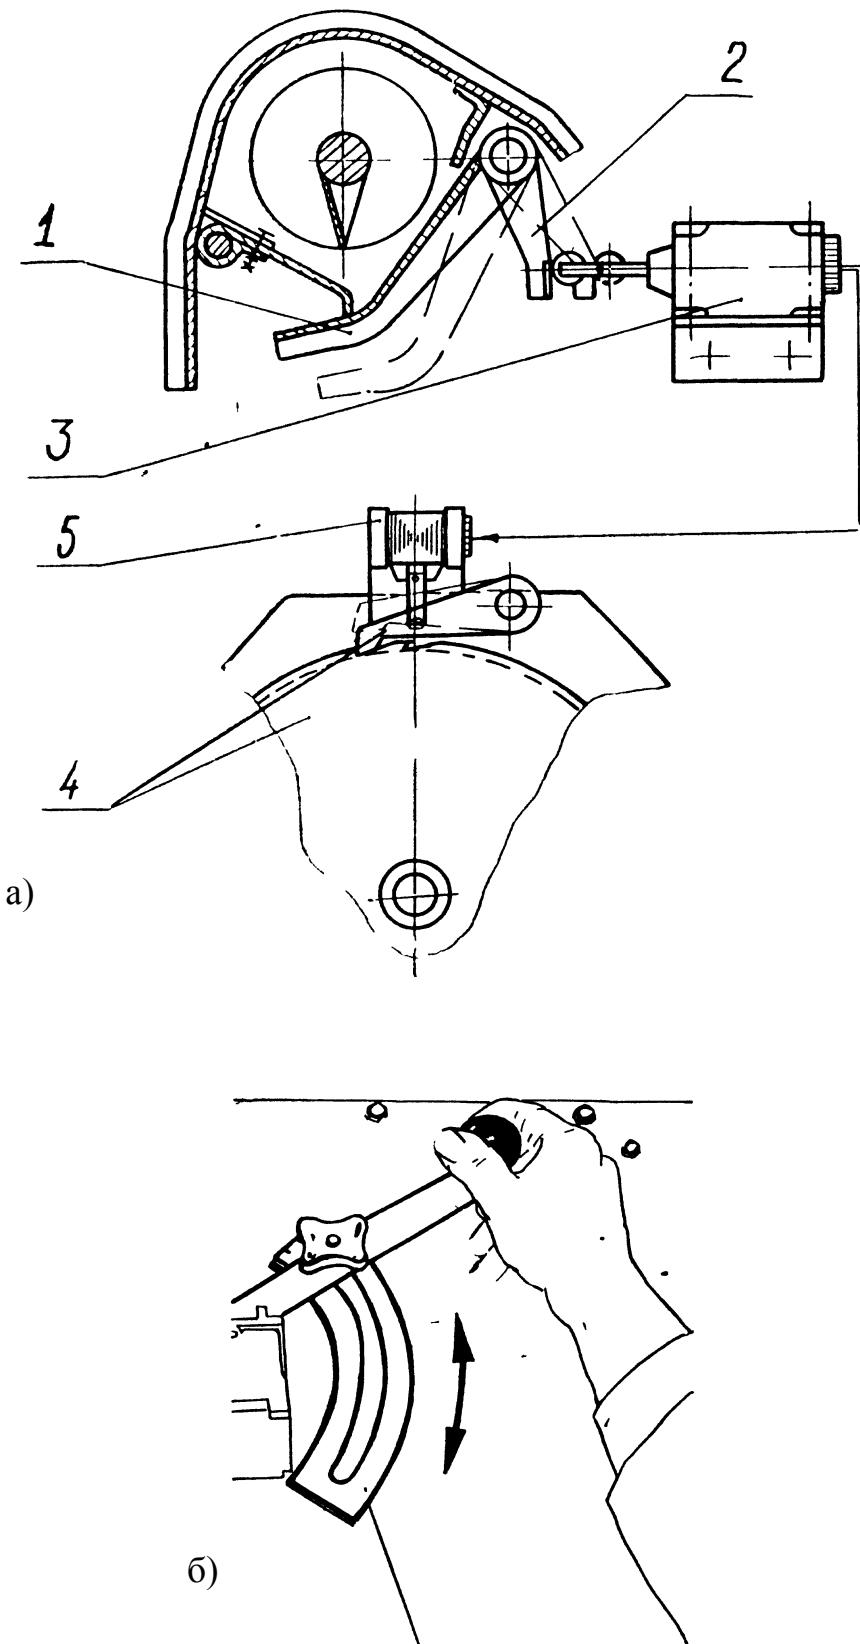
Регулировки загрузки машины. а – автоматический регулятор загрузки; б – регулировка усилия поджатия клапана. 1 - клапан-питатель; 2 - отключающий упор; 3 – выключатель; 4 - механизм самопередвижения; 5 - электромагнит.
